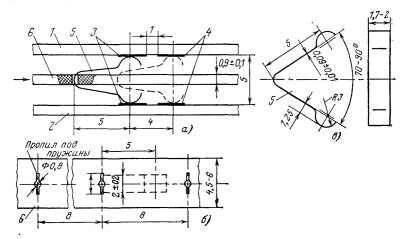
Конструкция двухплатного кнопочного переключателя.
